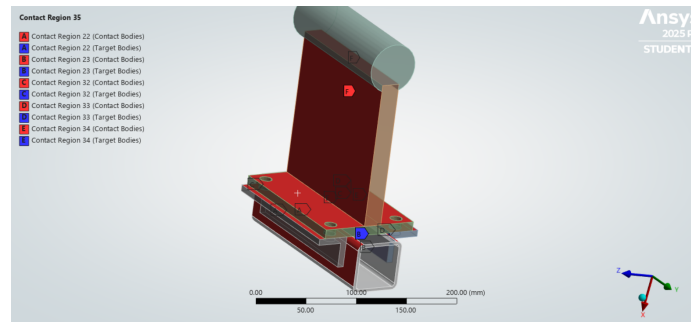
Contactos *bonded* simulando soldadura, segundo yunque
